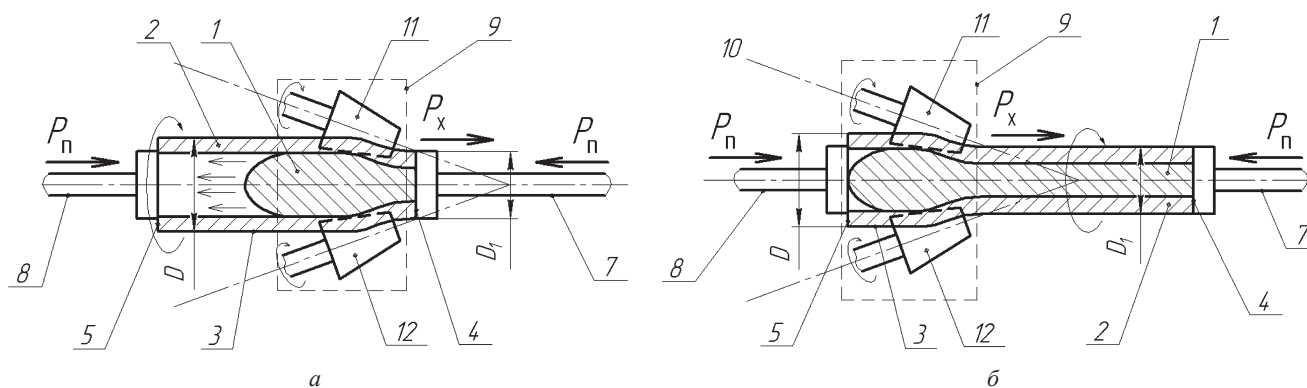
Поперечно-винтовая прокатка слоистых металлических заготовок на трехвалковом стане с подпором торцов пакета: а – начальная стадия прокатки; б – конечная стадия прокатки
